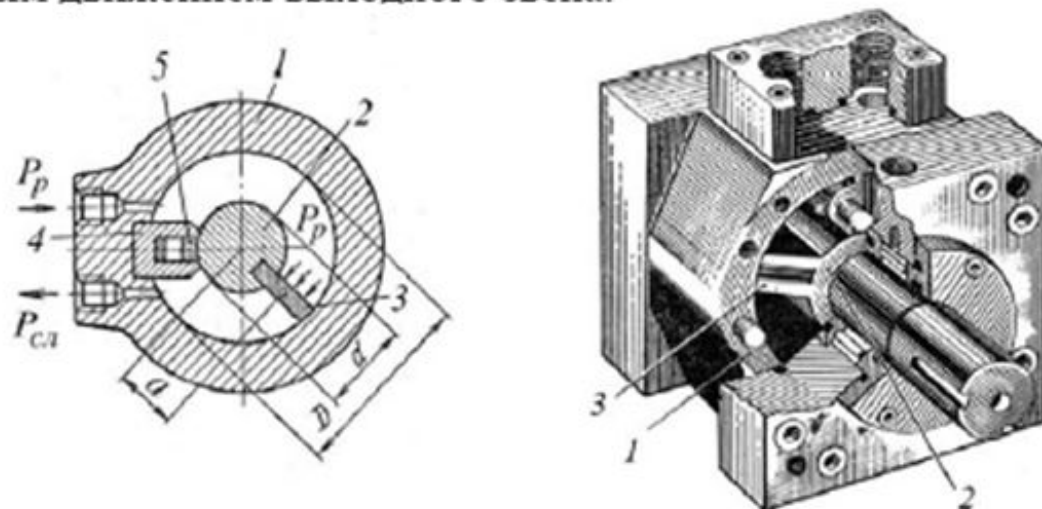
Поворотный однолопастной гидроцилиндр:
